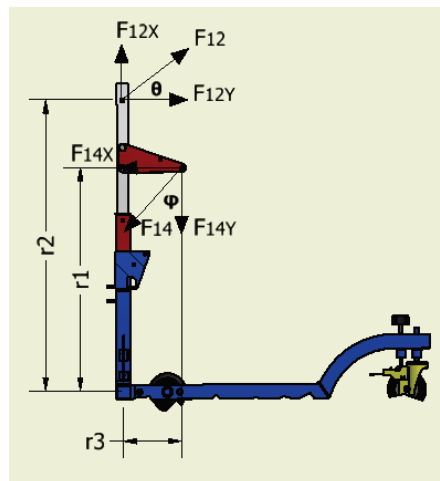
Fuerzas actuantes generadoras de torque en barra transversal de estructura base.
